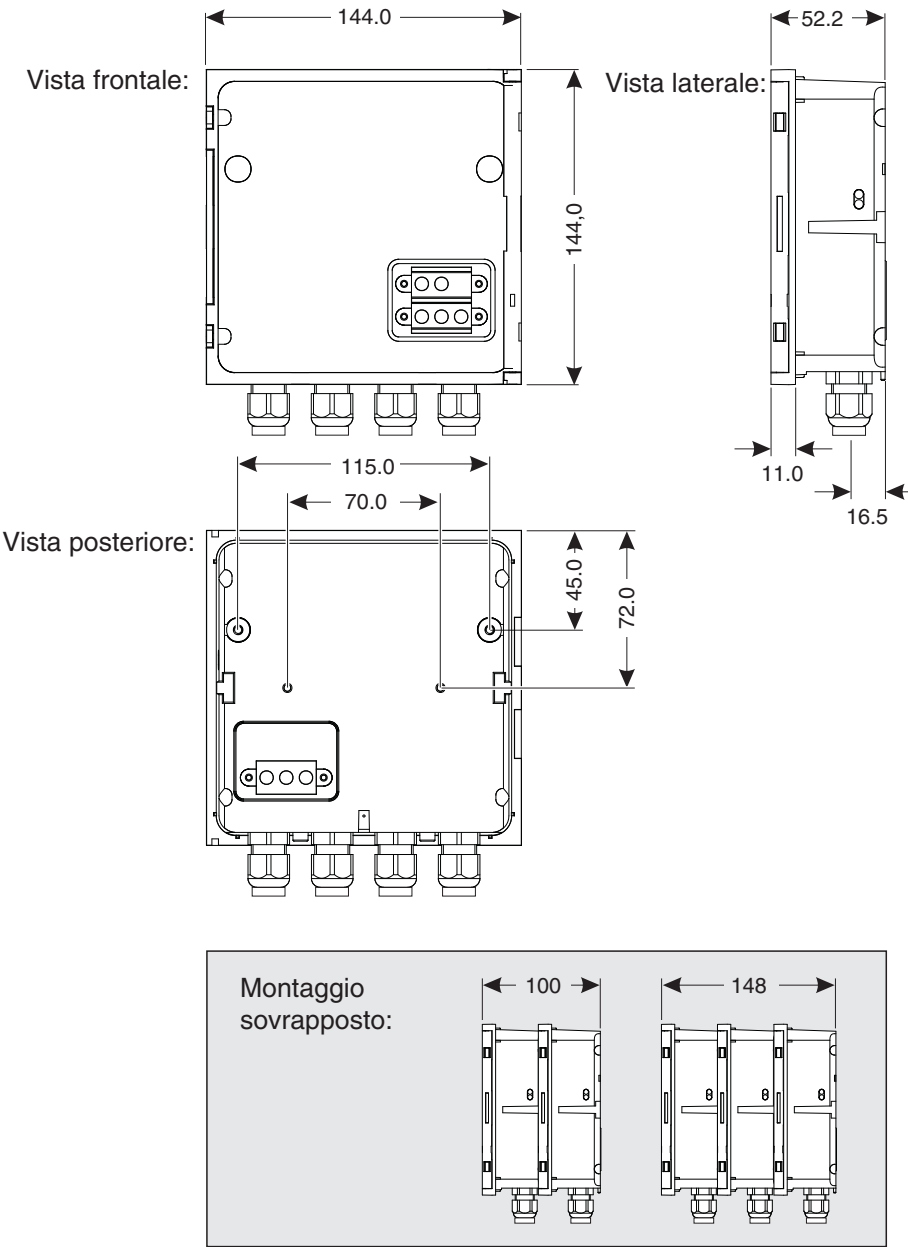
Disegno dimensionale per modulo MIQ (dimensioni in mm)
